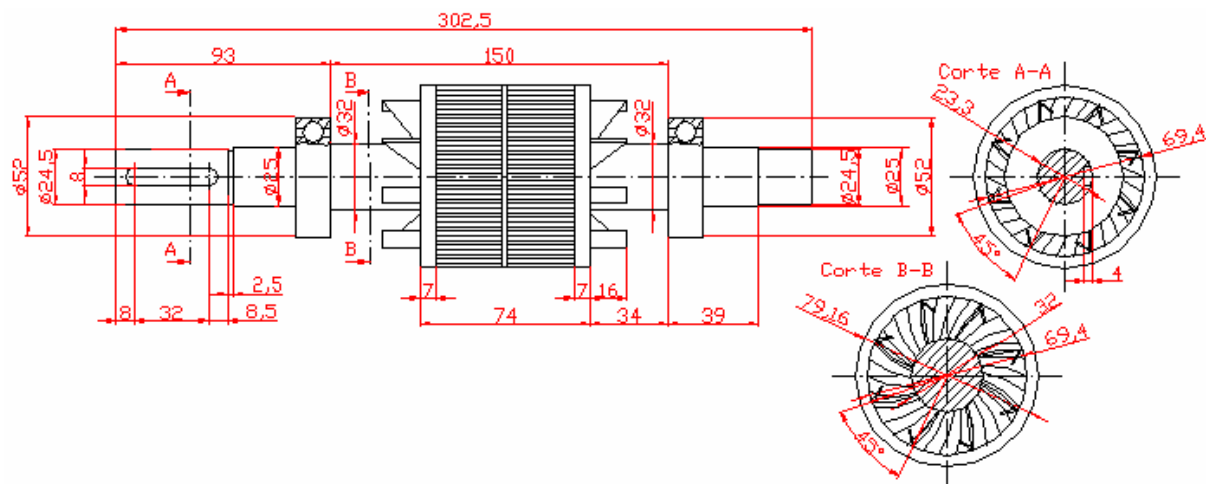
Vista lateral y en planta del rotor de chapas tipo B. Las cotas están dadas en mm.
